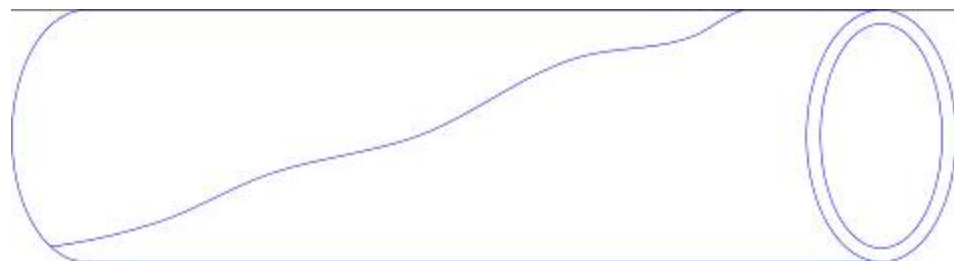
Прокатная единичная плена, расположенная на наружной поверхности трубы, образующаяся при раскатывании заката, закова, имевшегося на заготовке
